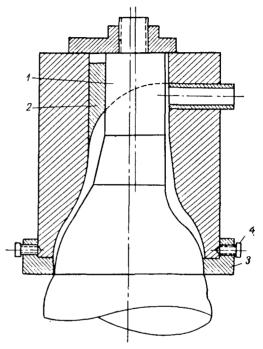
Головка с боковым питанием: 1—дорн; 2—направляющая втулка; 3—формующее кольцо; 4—регулировочный болт; 5—штупер для входа расплава.
